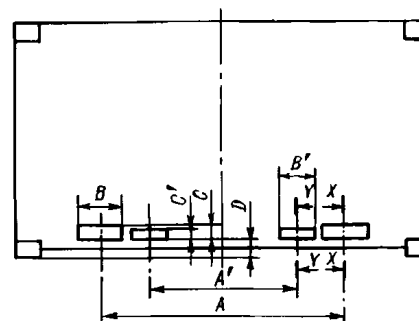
Расположение и размеры карманов для вилочных захватов
